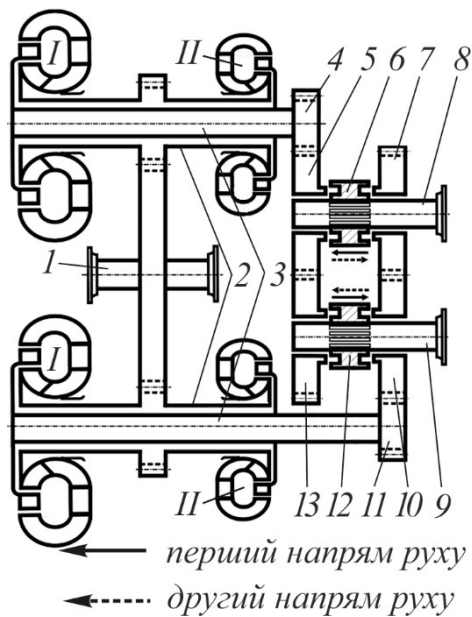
Схема багатопотокової багатшвидкісної гідравлічної передачі із шістьма реверсивними шестірнями: I – пусковий ГТР; II – маршовий ГТР; 1 – вхідний вал; 2 – насосний вал; 3 – турбінний вал; 4, 5, 7, 10, 11, 13 – реверсивні шестірні; 6, 12 – кулачкові муфти; 8, 9 – вихідні вали
